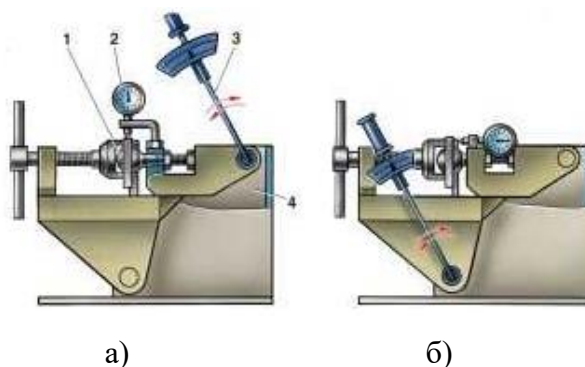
Проверка шарового шарнира на приспособлении 02.8701.9502:
